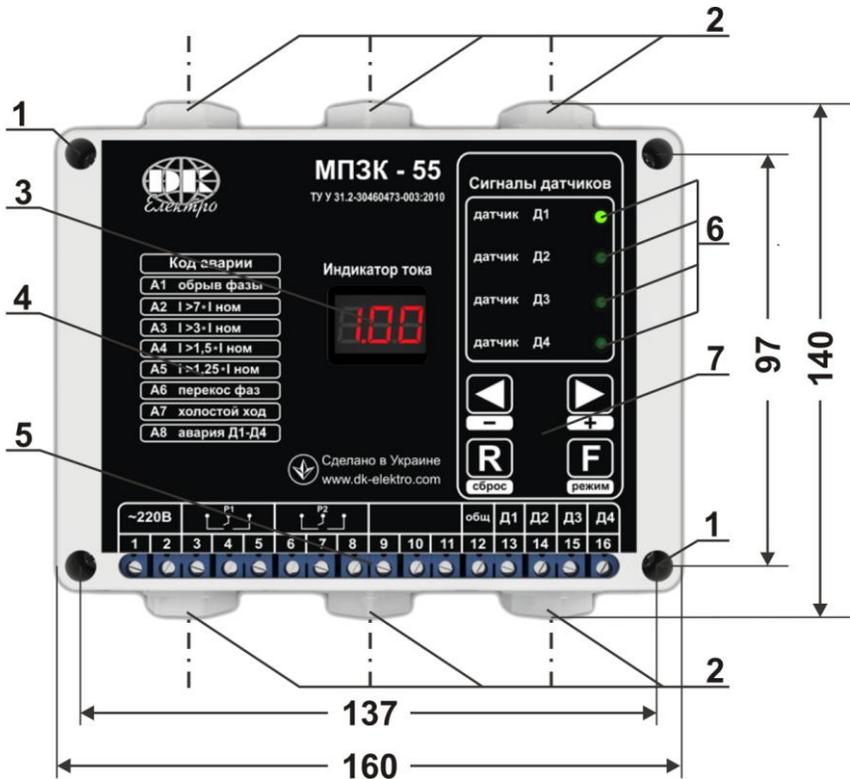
Внешний вид. Габаритные и установочные размеры прибора.
